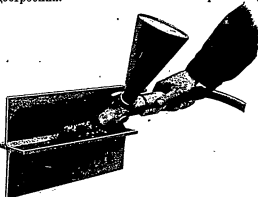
Держатель ДШ-5 при сварке углового шва
